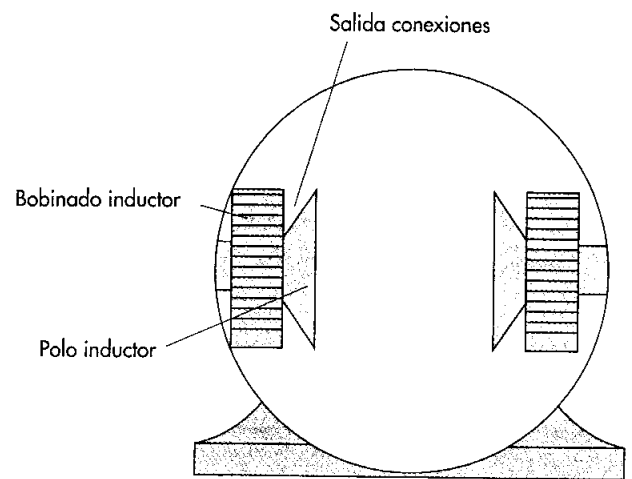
Puntos frecuentes de contactos a masa del bobinado inductor.
